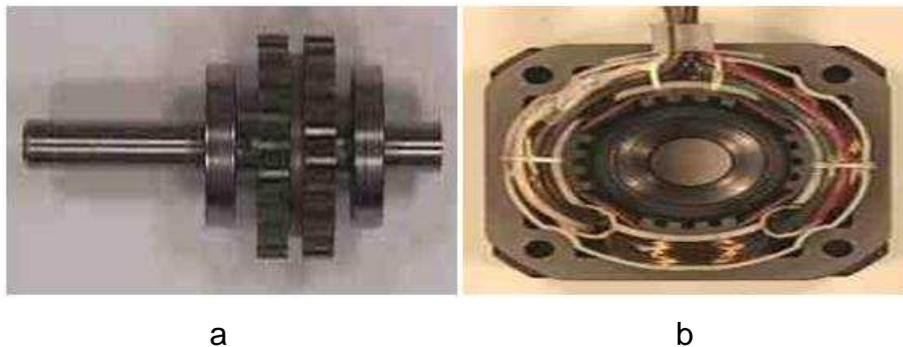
a) Imagen del rotor b) Imagen de un estator de 4 bobinas
